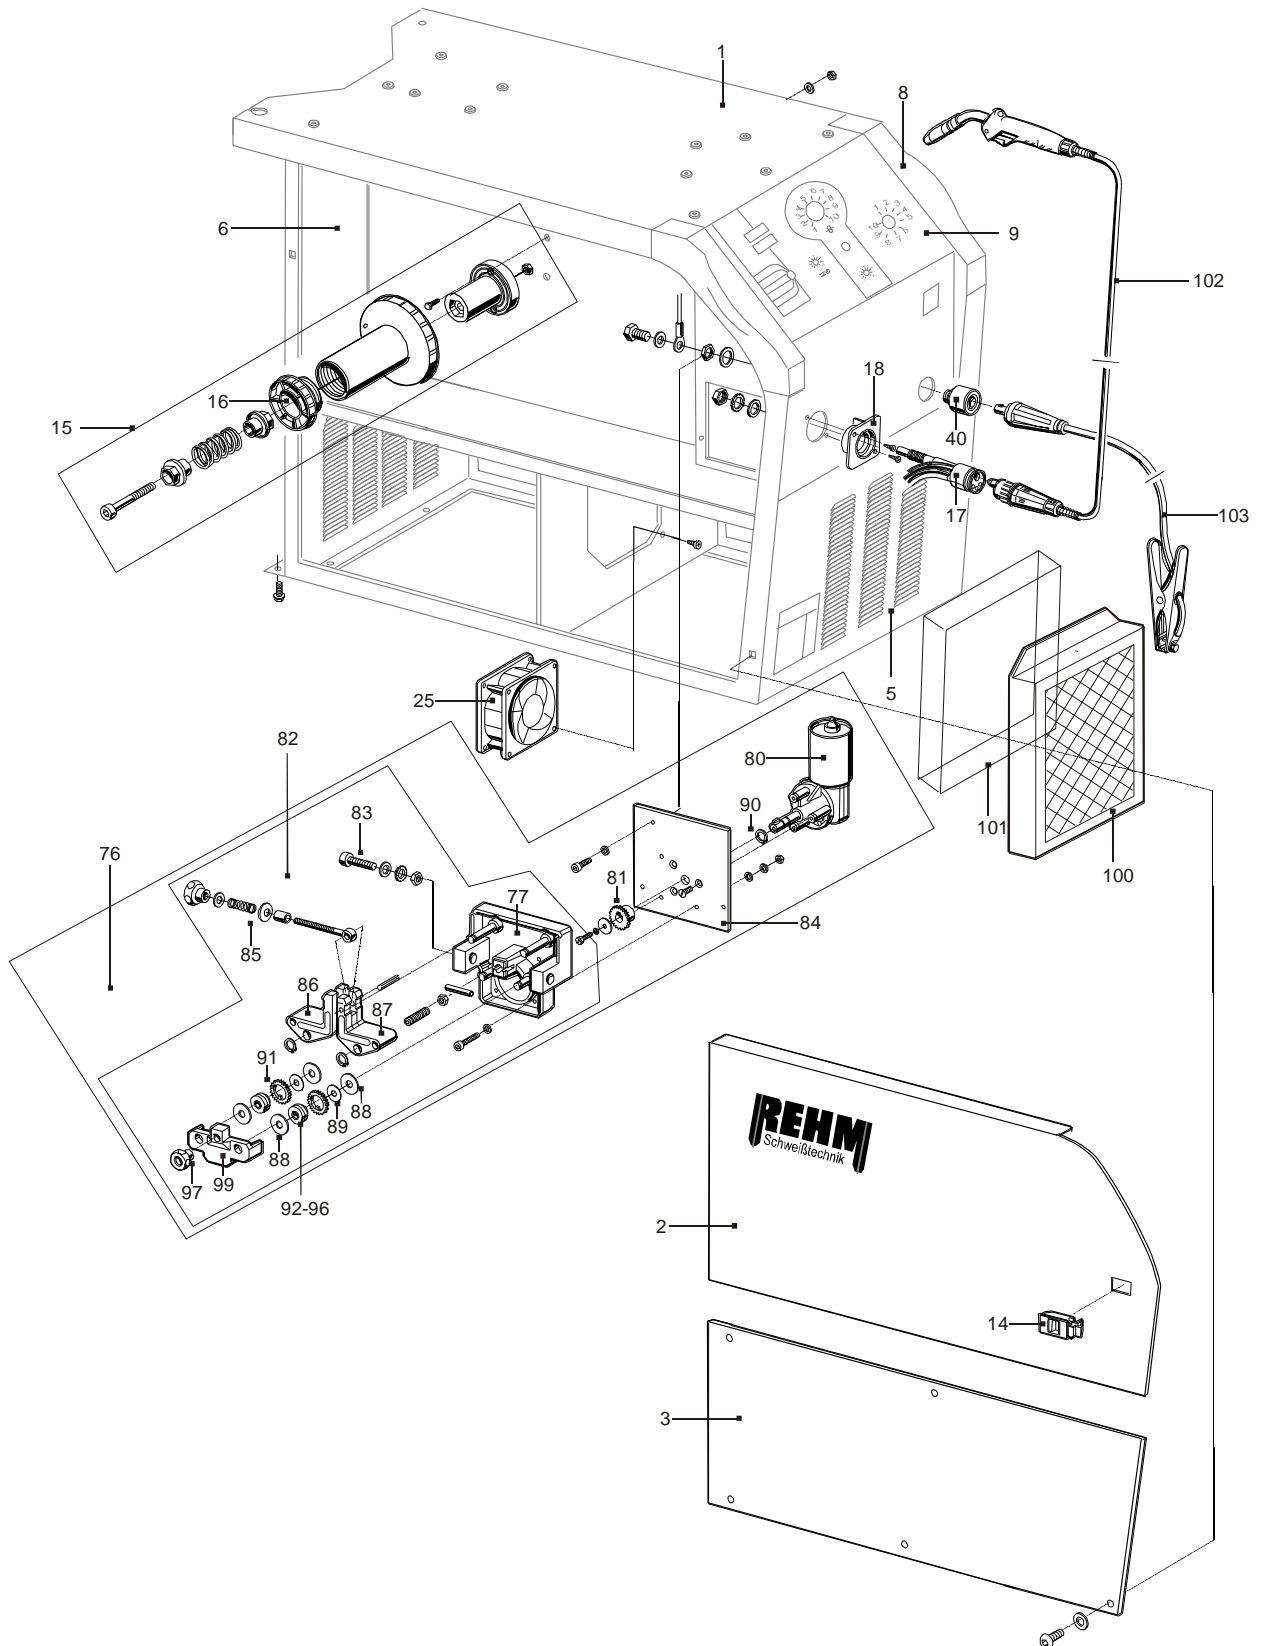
Explosionszeichnung SYNERGIC.PRO² 250-4 – 450-4W (links)
